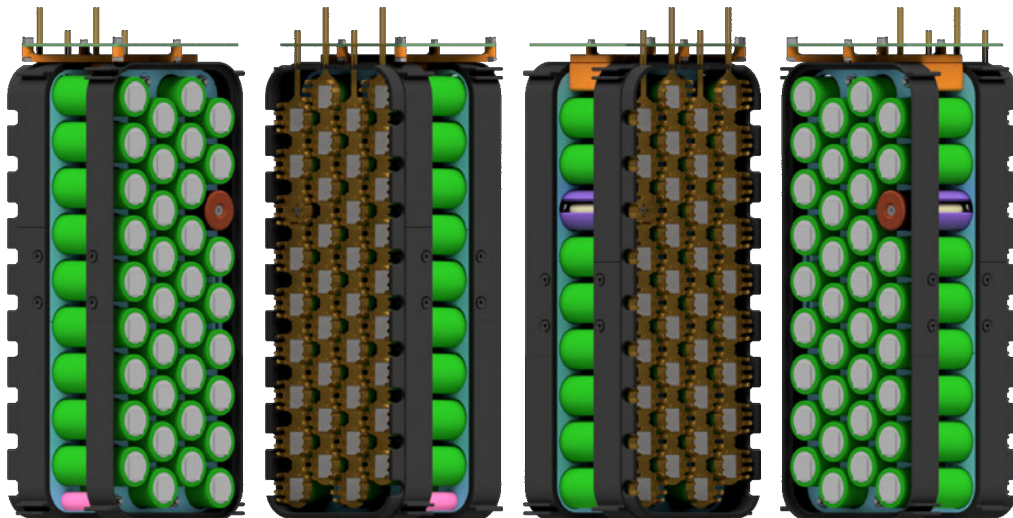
Rendering des nachgebauten Batteriemoduls
